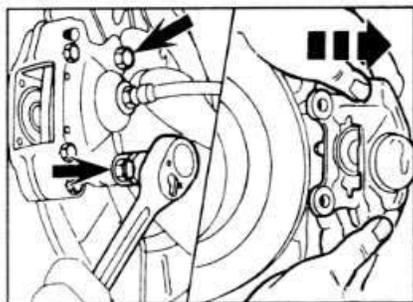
Расположение болтов крепления заднего суппорта.
